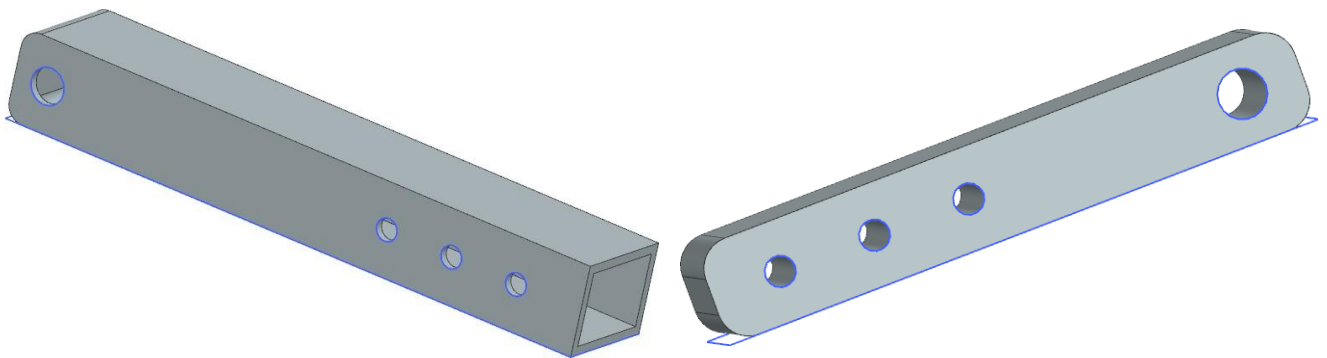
y 47. Diseño en CAD del diseño del brazo.
